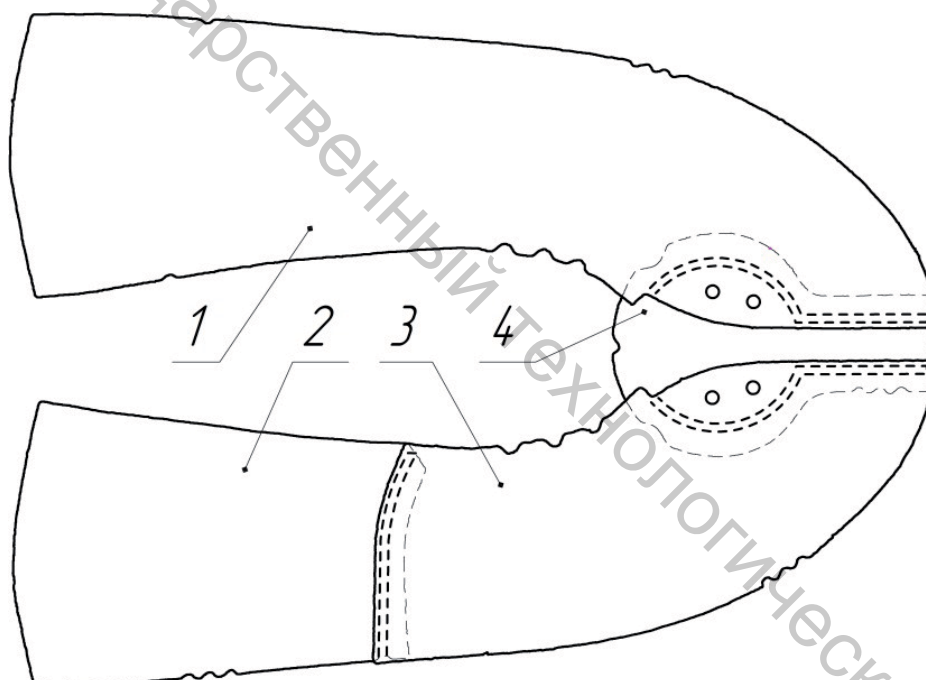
Схема заготовки верха туфель дошкольных для девочки
